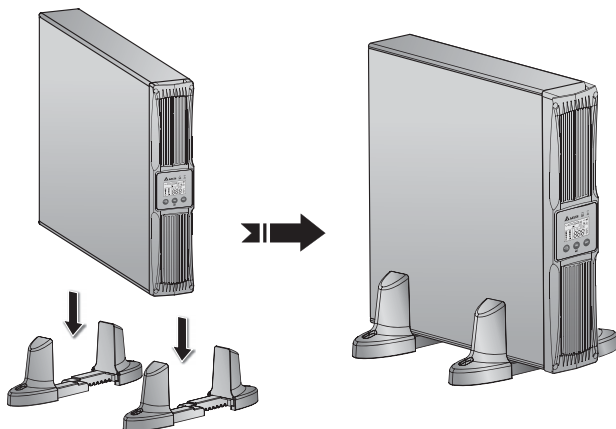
Montaż podstawek do ustawienia zasilacza UPS w konfiguracji Tower (opcjonalne))
